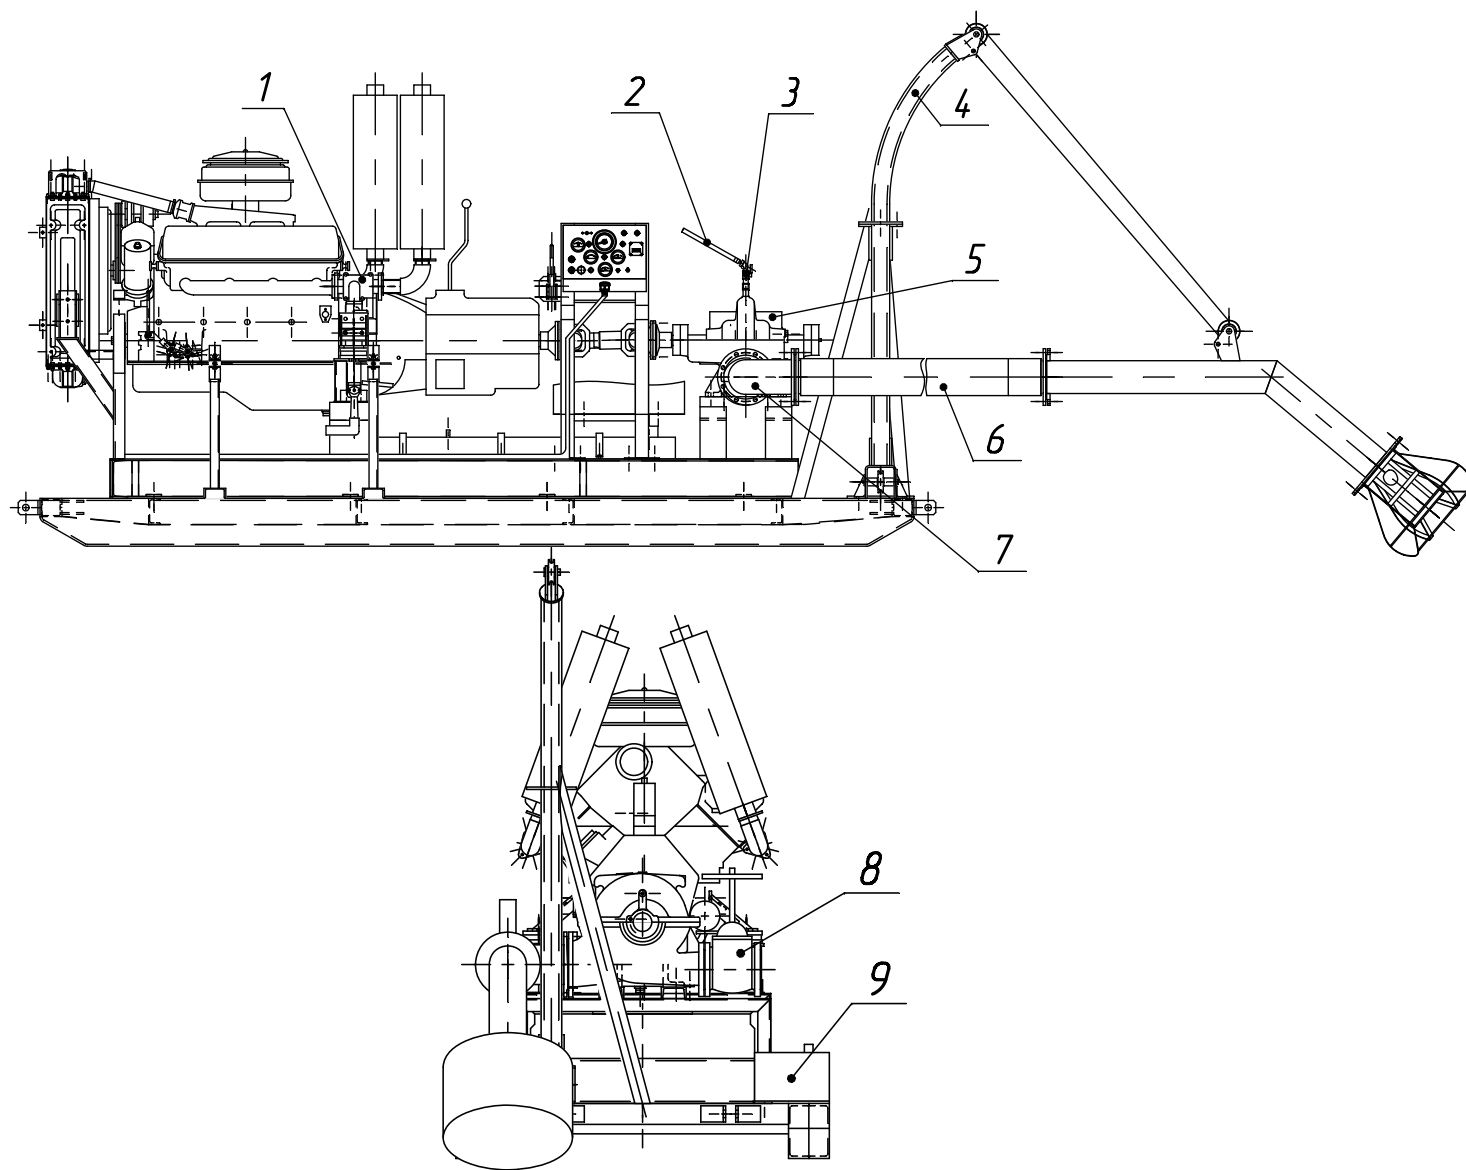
Общий вид агрегатов типа ДНА-п
